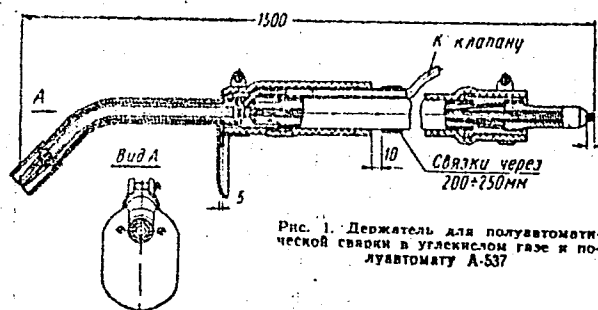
Держатель для полуавтоматической сварки в углекислом газе к полуавтомату А-537
